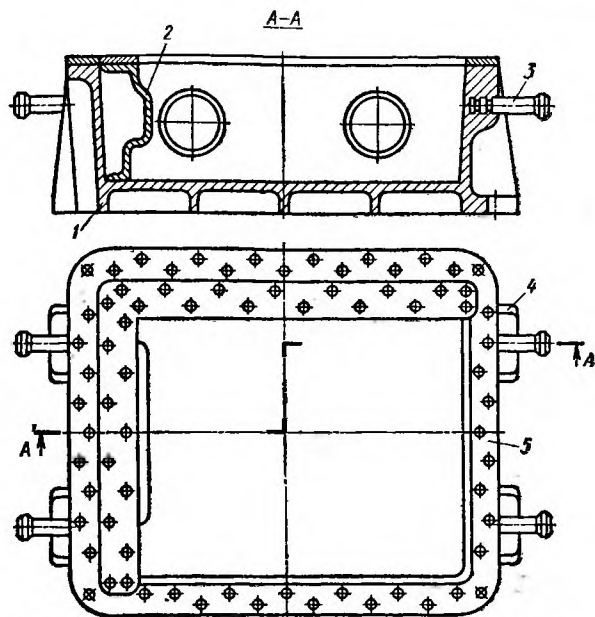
Металлический ящик для встряхивающих машин: 1 — корпус; 2 — вкладыш; 3 — цапфа; 4 — приливы для крепления ящика к столу машины; 5 — броня
